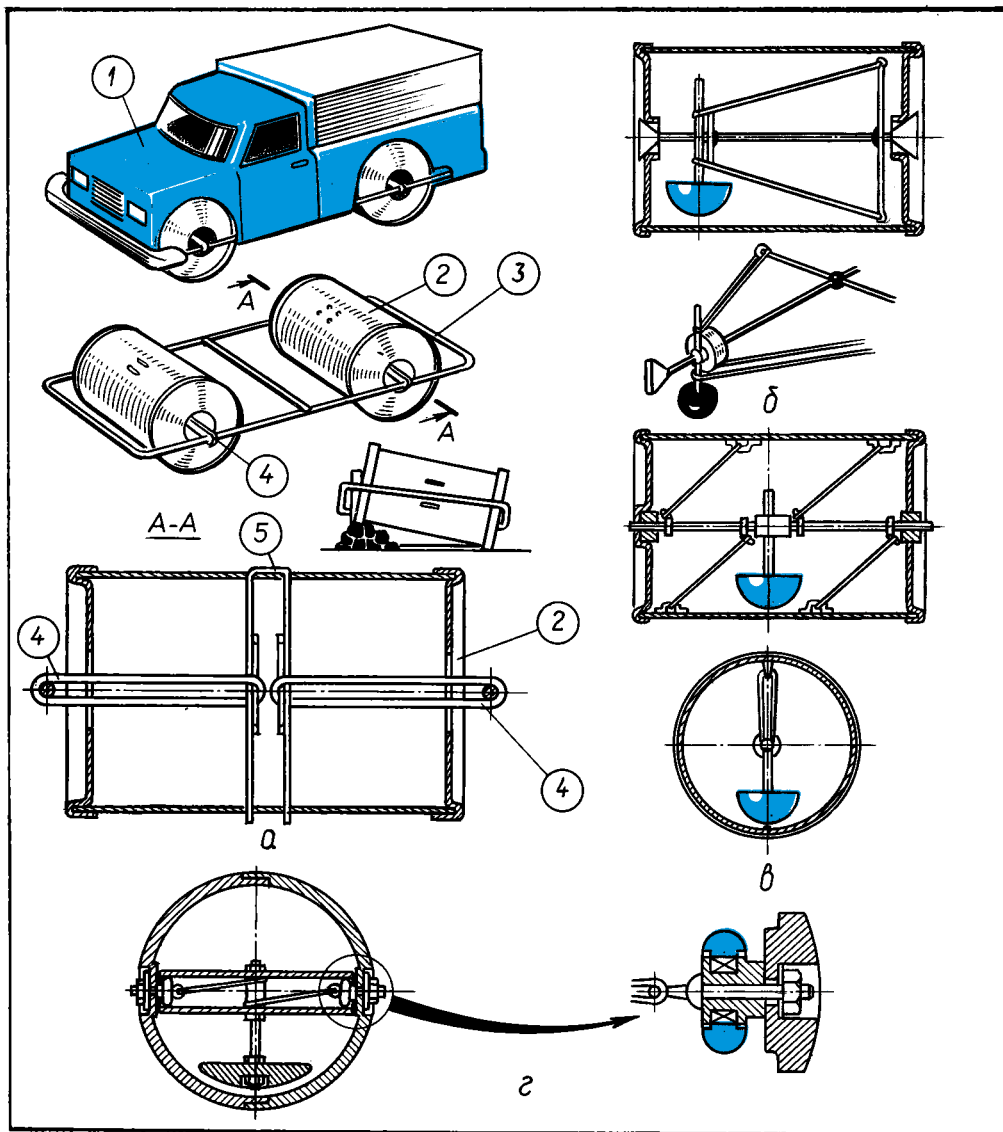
Четыре конструкции мотор-колеса: 1— кузов модели; 2— колесо; 3— рама; 4— резиновый двигатель; 5— скоба.
